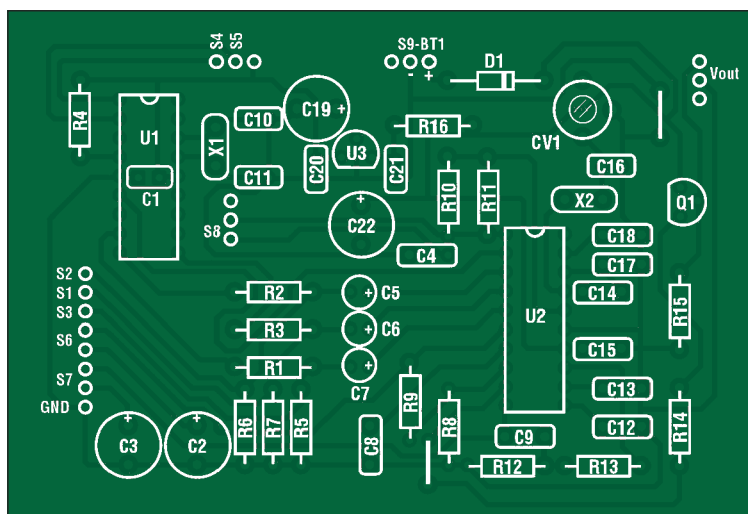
PCB lato componenti del generatore video in scala 1:1.
